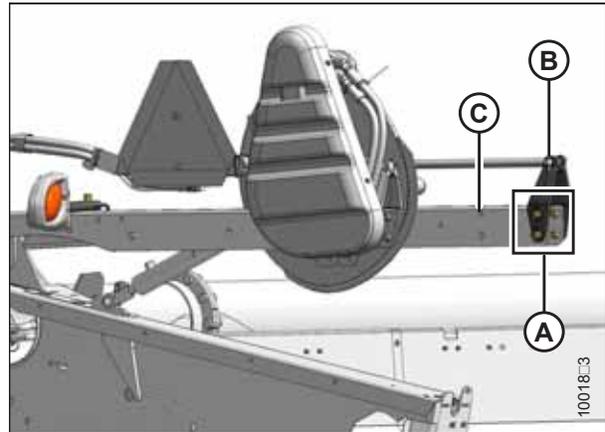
Rechter Haspel-Horizontalzylinder in Stellung „Vorne“
